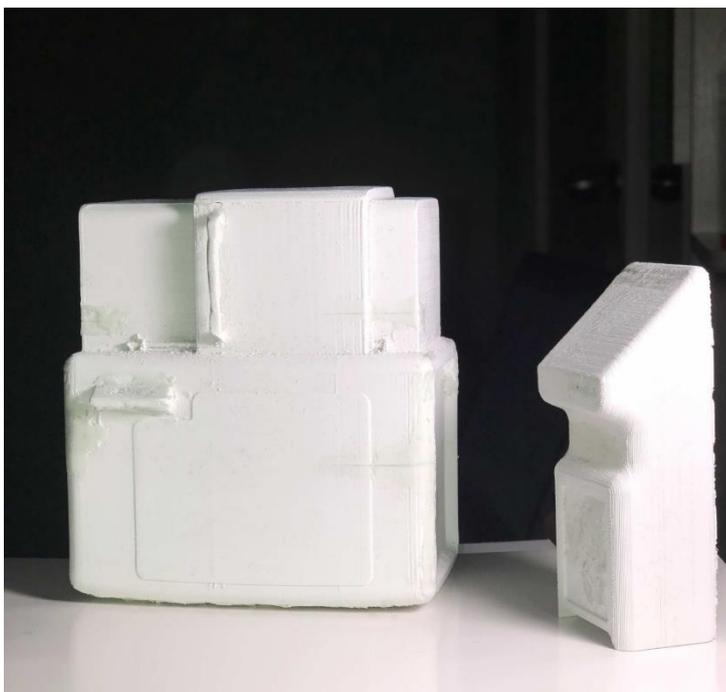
Готовый макет корпуса стенда и стойки управления
